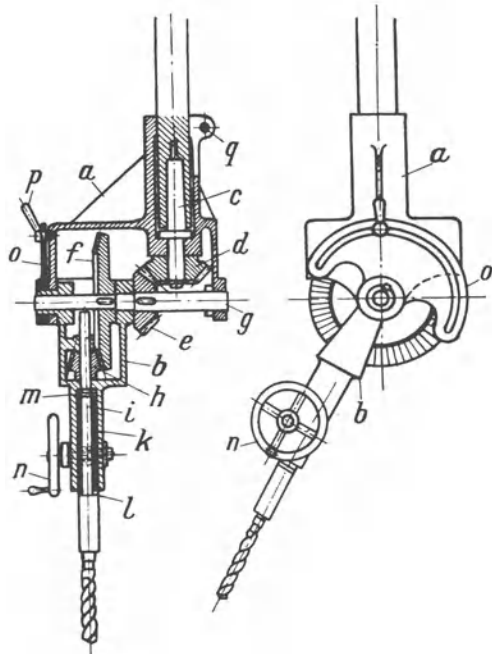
Bohrapparat mit radial ausschwenkbarer Spindel.
